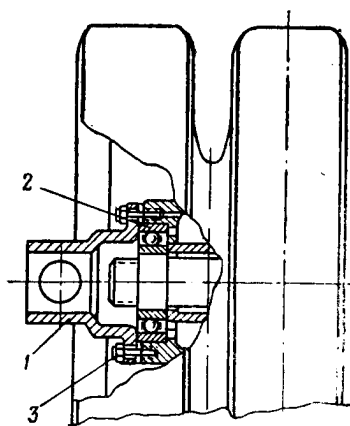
Установка катка: 1 — ключ; 2 — подшипник; 3 — болт.
